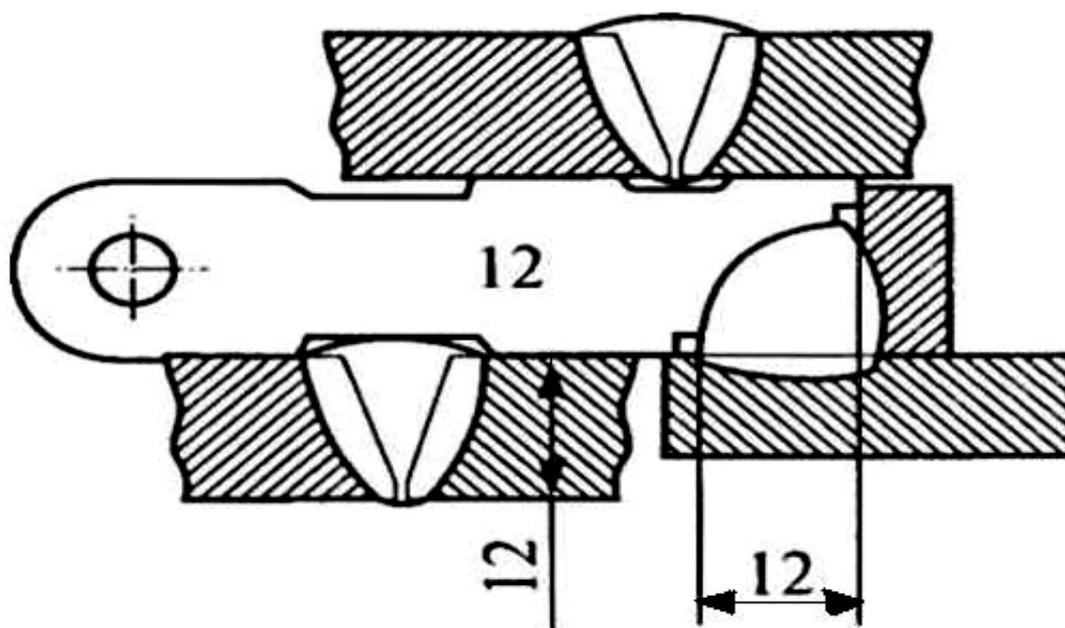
Специальный шаблон для контроля сварных швов
